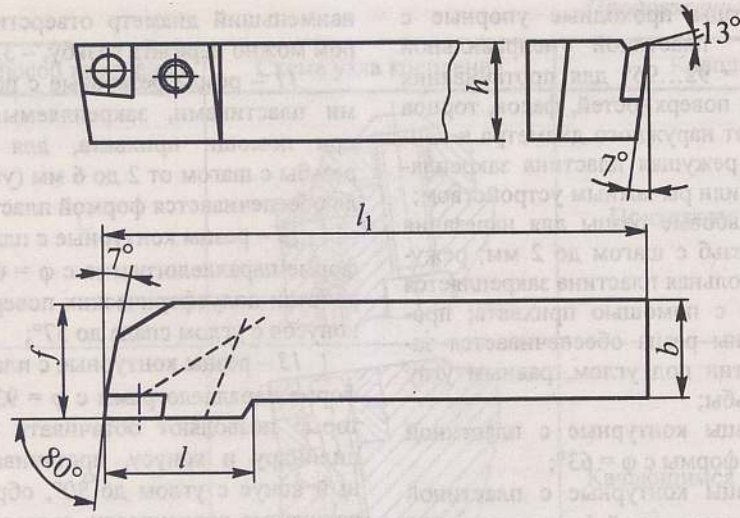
Токарный резец с тангенциальным креплением СМП
